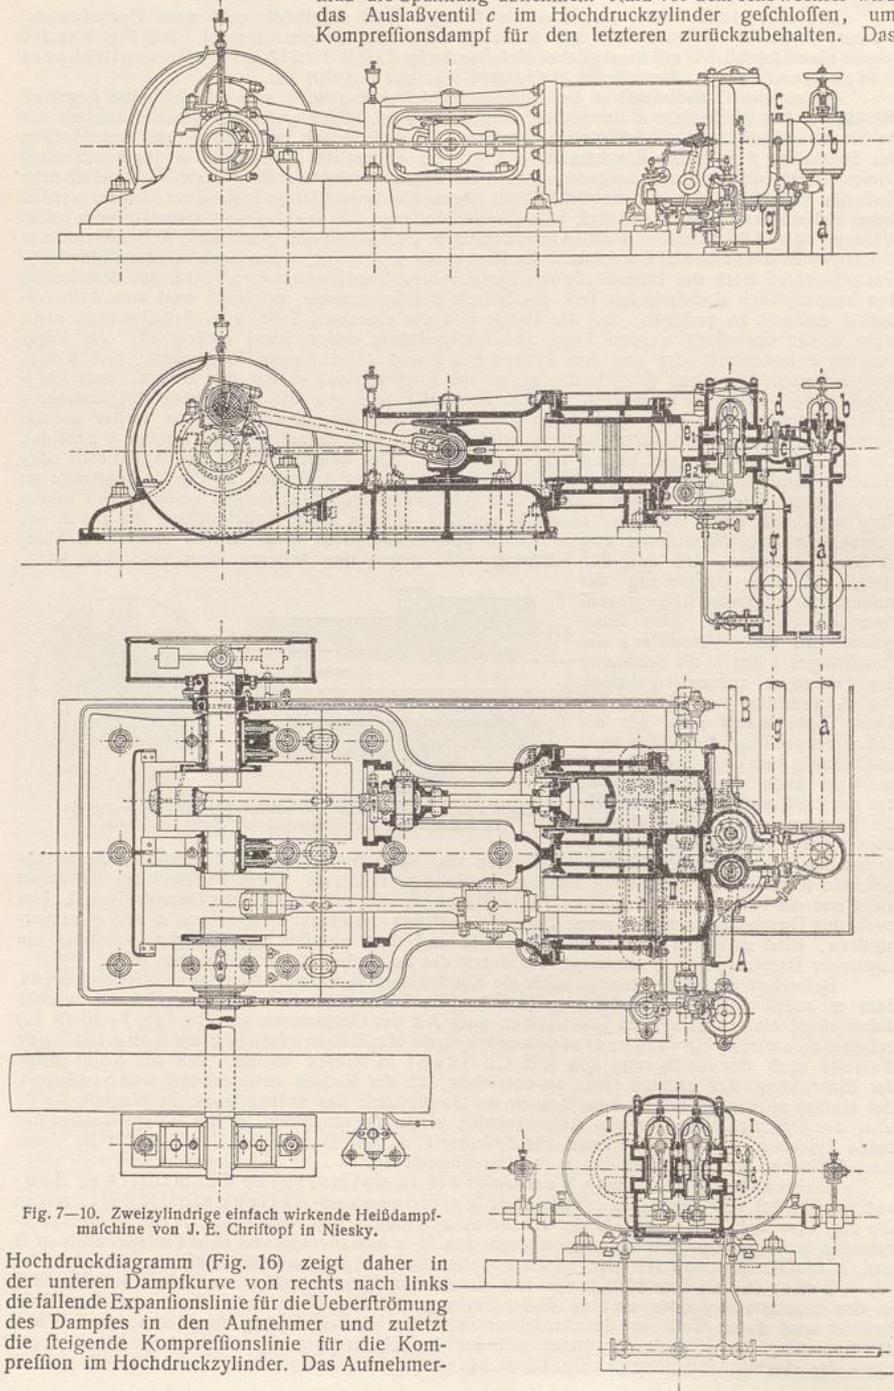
10. Zweizylindrige einfach wirkende Heißdampfmaschine von J. E. Christopf in Niesky.
